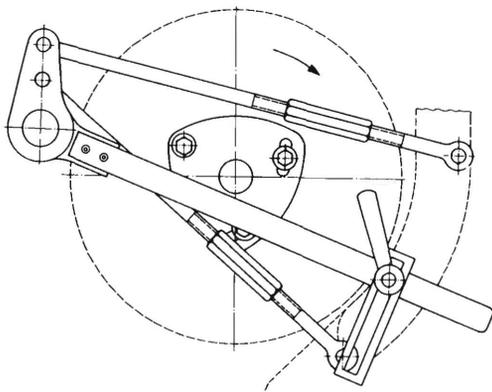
Schnellverstellvorrichtung des Munkells-Mähreschers.
